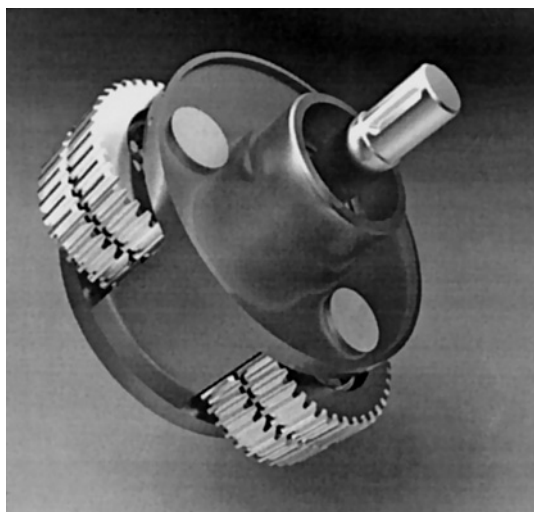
Блок сателлитов планетарной передачи механизма вытягивания слитков установки полунепрерывной разливки стали
